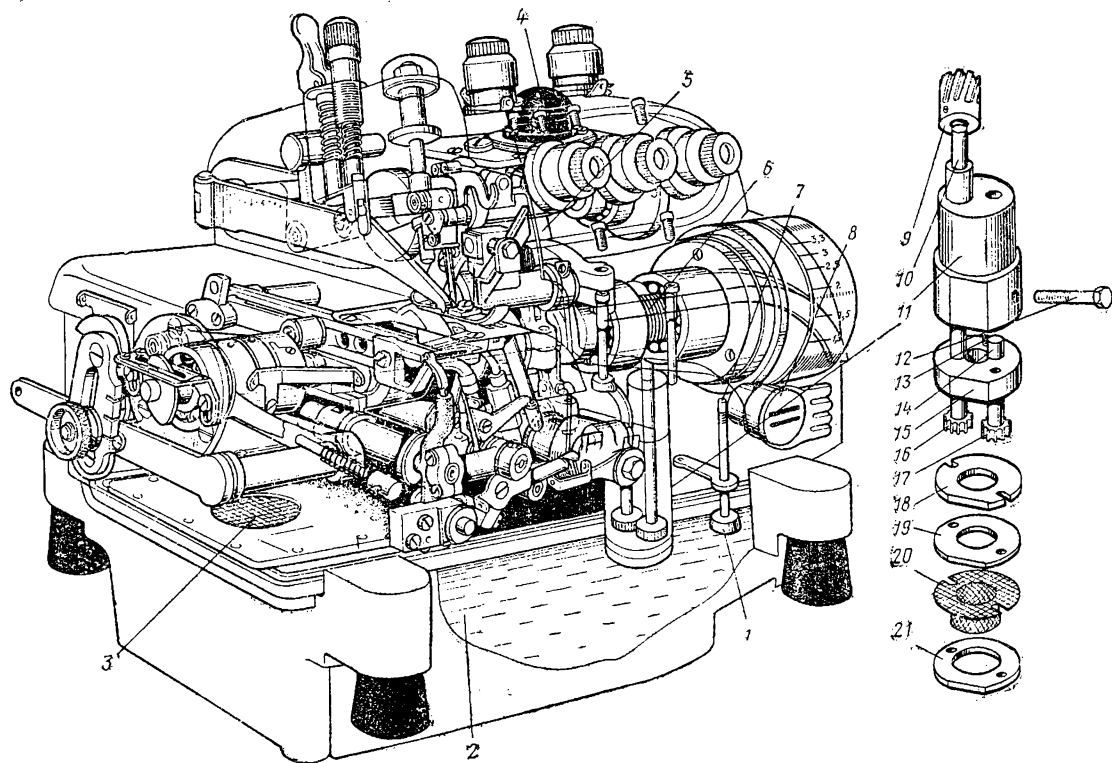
Система автоматической смазки механизмов машины 408-А кл.
